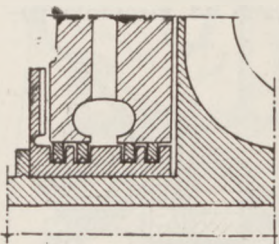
Osłowa wirnika sprężarki Pratt & Whitney z łożyskowaniem czysto tocznym i przejściem sił osiowych za pomocą łożyska kulkowego.
